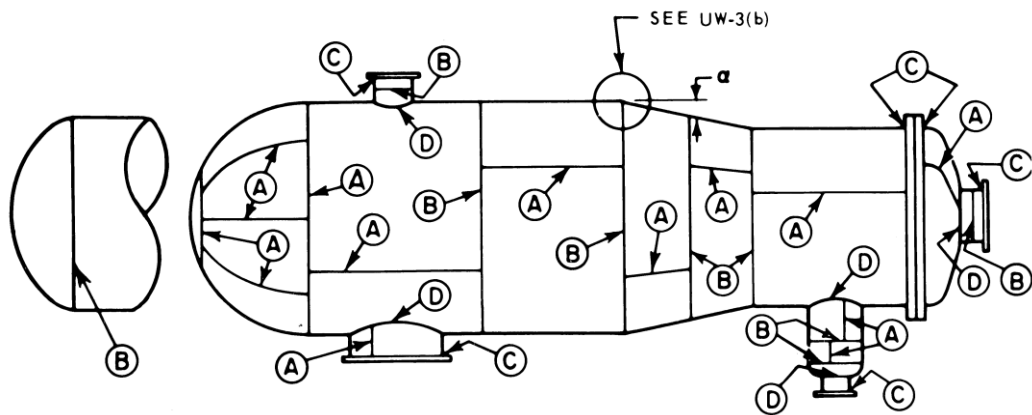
representación de la categorización de la soldadura. Fuente: [37]
